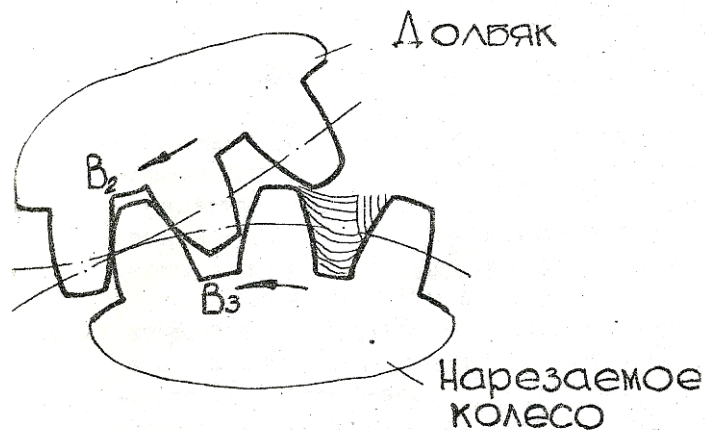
Профили зубьев долбяка и заготовки и схема снятия припуска
